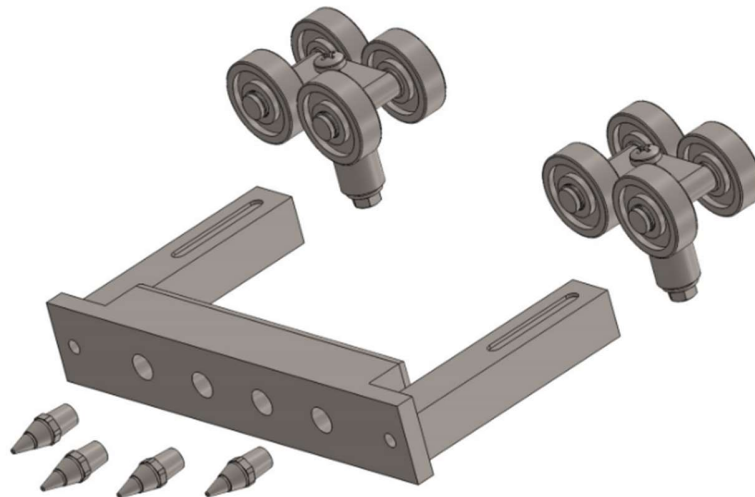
Conjunto expulsor de aire comprimido--Vista explosionada.
